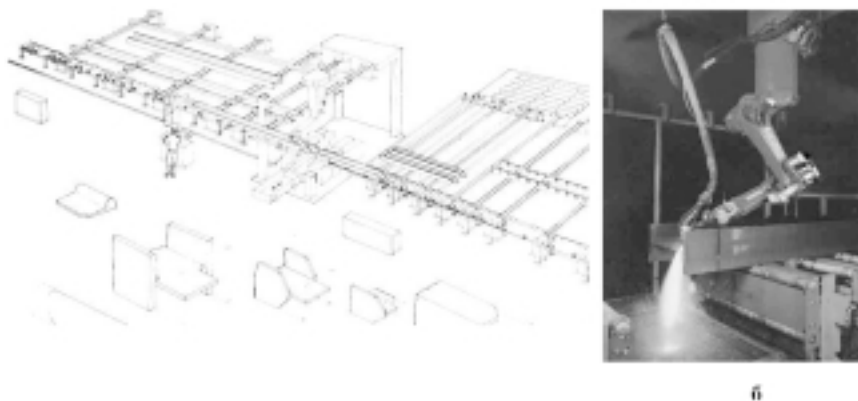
Автоматизированная линия вырезки деталей из профильного проката: а – общий вид линии резки профиля; б – робот-резчик сварного и профильного проката
